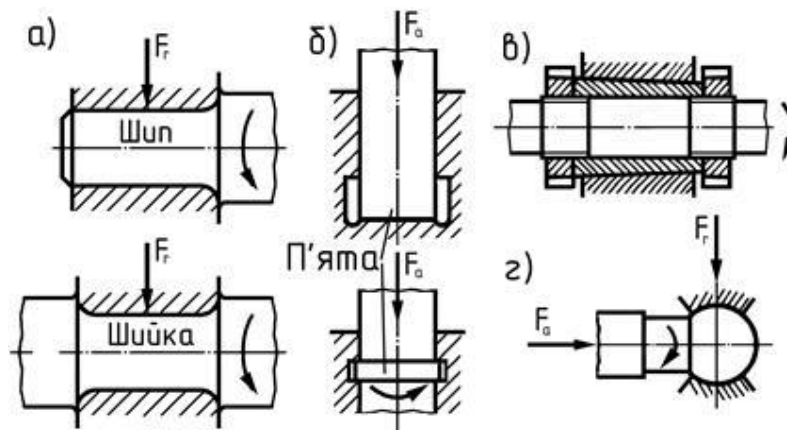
Форма робочої поверхні підшипників ковзання циліндричною (а), плоскою (б), конічною (в), сферичною (г)
